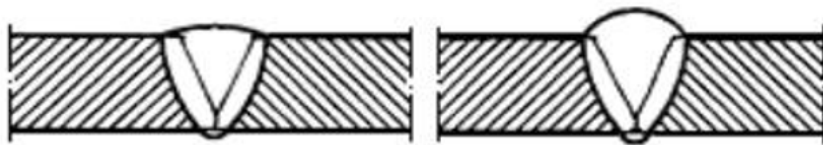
Эскиз дефекта сварного шва
